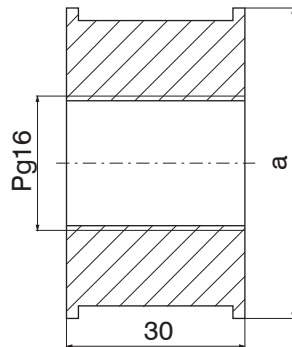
Maßzeichnung Cleaner (Abmessungen in mm, nicht maßstabsgetreu)
